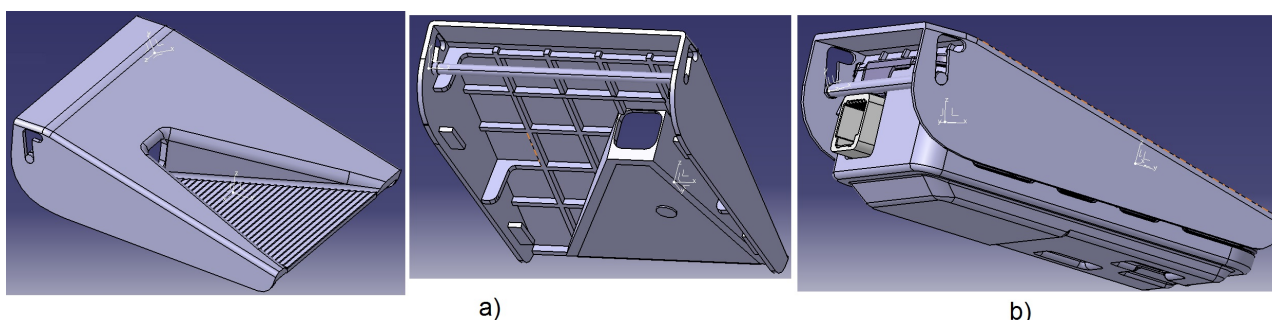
Varianta constructivă a III-a a bracketului (suportului) pentru camera video fixată pe parbrizul automobilului
